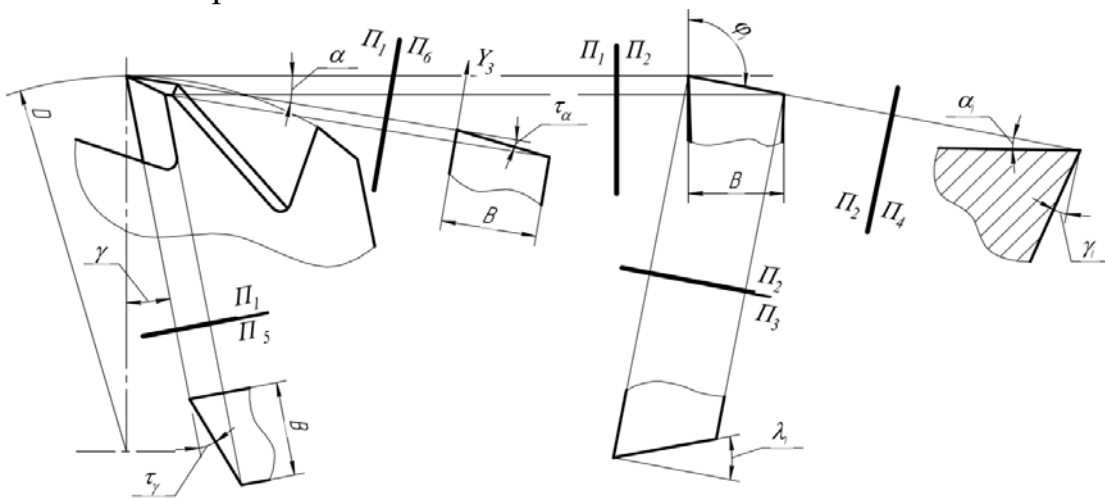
Конструктивні та геометричні параметри відрізної фрези з різнонаправленими зубцями
